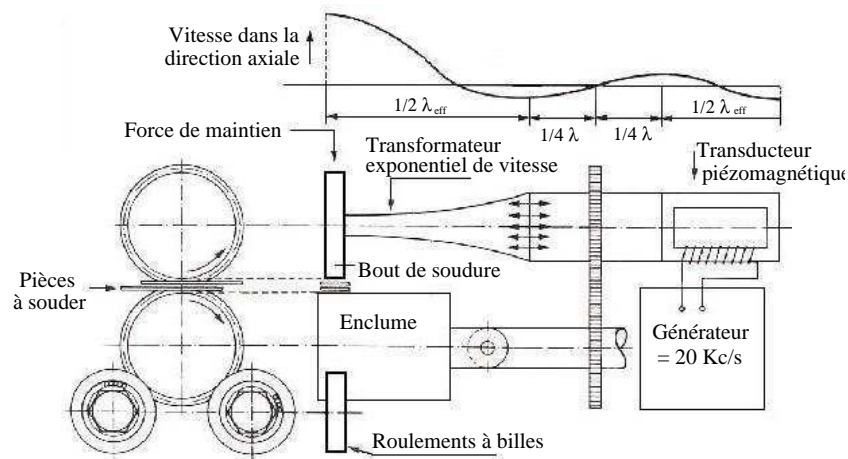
Deuxième configuration de l'ensemble acoustique pour la technique de soudage des métaux [4]
